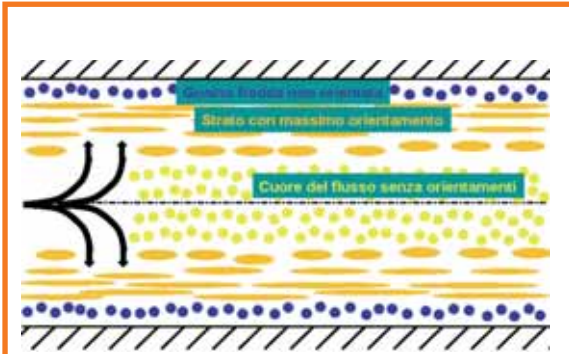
Orientazione longitudinale massima vicino alle pareti dello stampo (non sulle pareti dove lo scorrimento è nullo)
